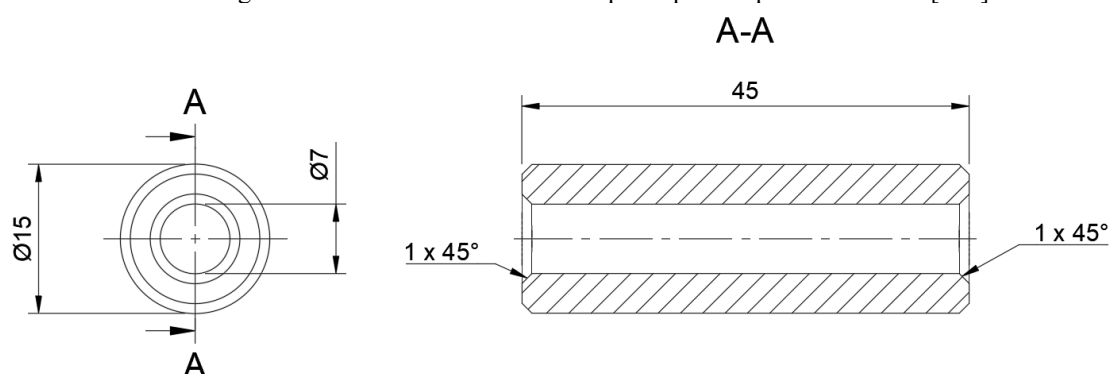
Desenho Técnico do corpo de prova tipo B cotado em [mm]
